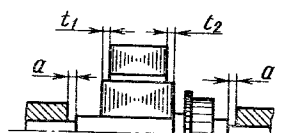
Осевой разбег ротора в подшипниках скольжения
